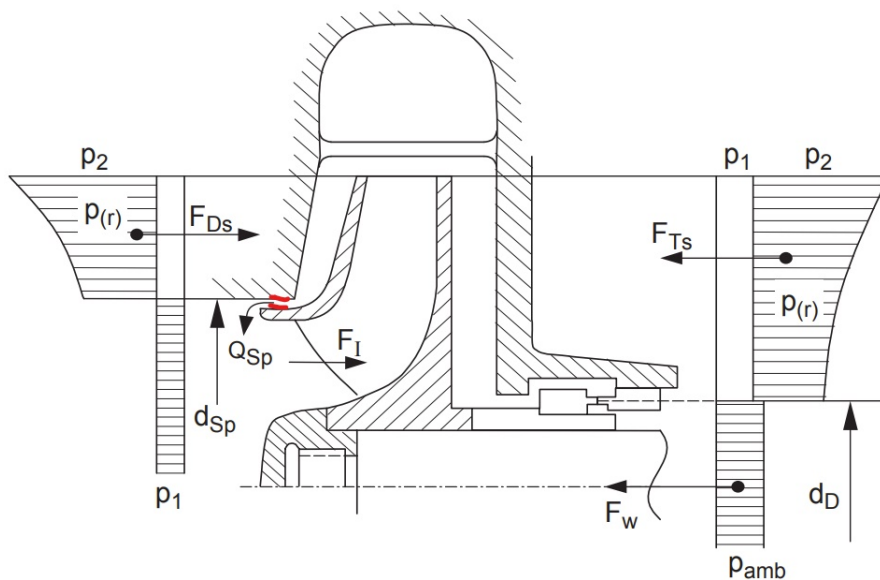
Axialkräfte am Pumpenlaufrad [11]
